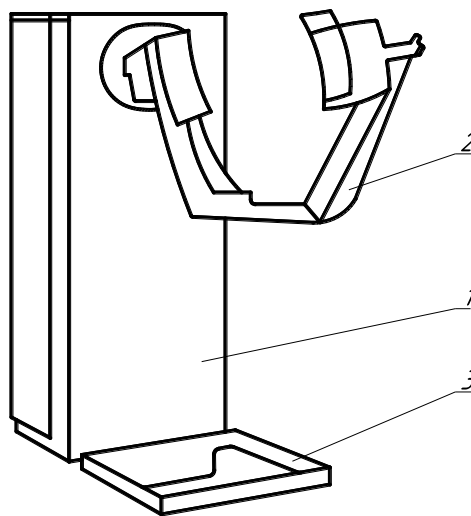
Стенд моделі Р 636: 1 – стійка; 2 – захват поворотний; 3 – піддон.
